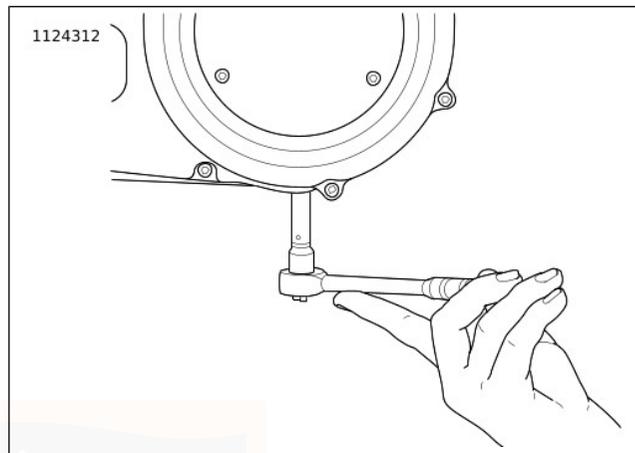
Extracción/instalación del tapón de drenaje del guardacadena
